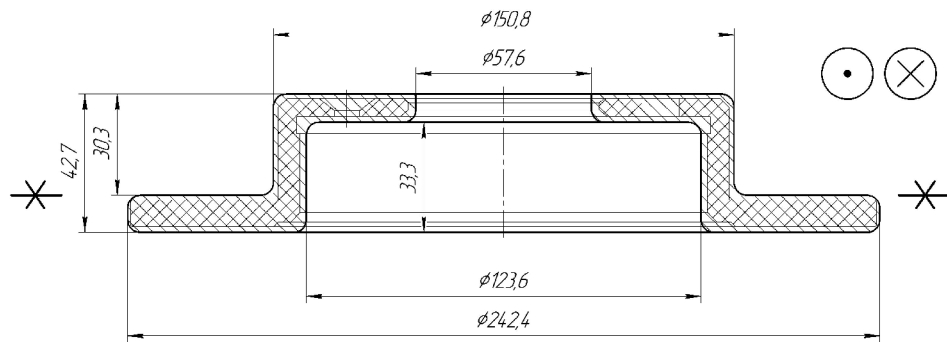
Ескіз заготовки, отриманої литтям в облицьований кокіль
